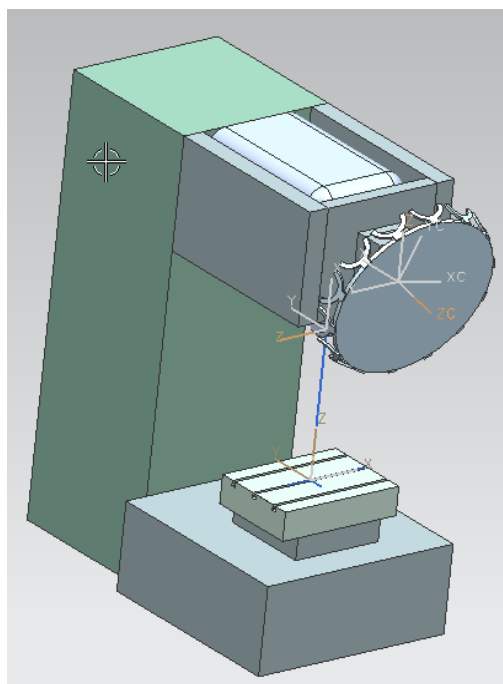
Разработанный симулятор станка Fanuc – Robodrill
